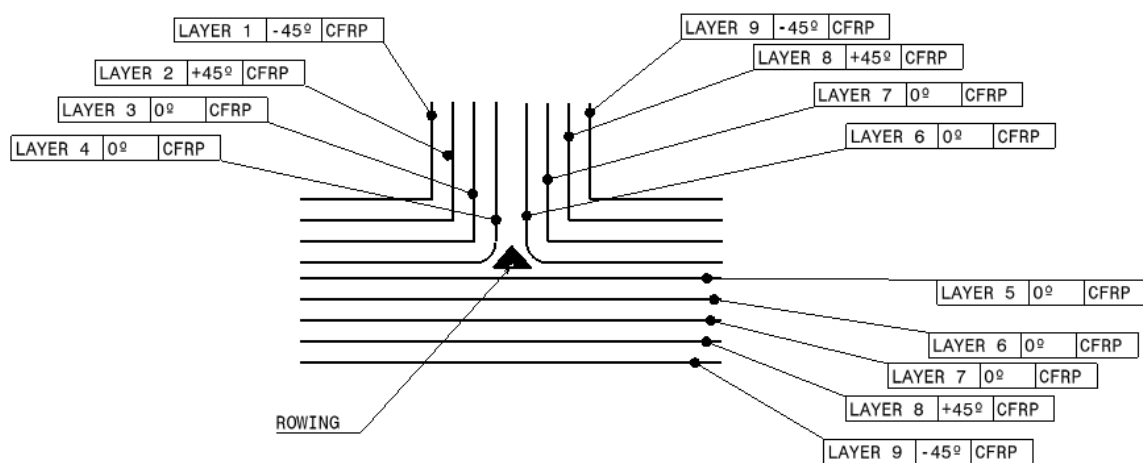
Esquema de apilado en refuerzos internos perfil en “T”
